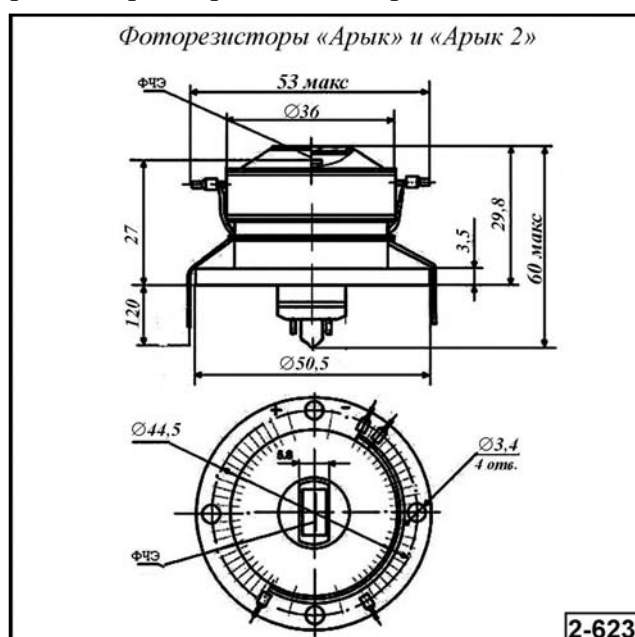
Внешний вид и габаритные размеры фоторезисторов «Арык» и «Арык 2»
